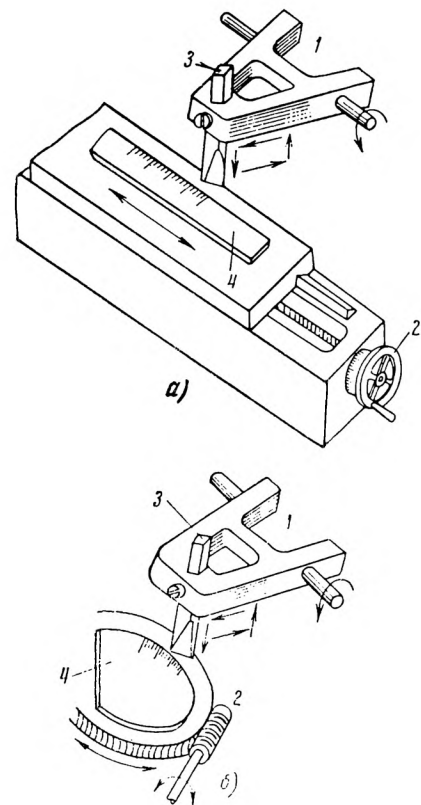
Схемы нанесения делений на продольной (а) и на круговой (б) делительных машинах
